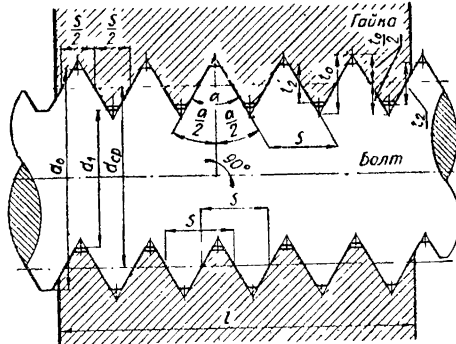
Профиль и основные параметры цилиндрической резьбы.
